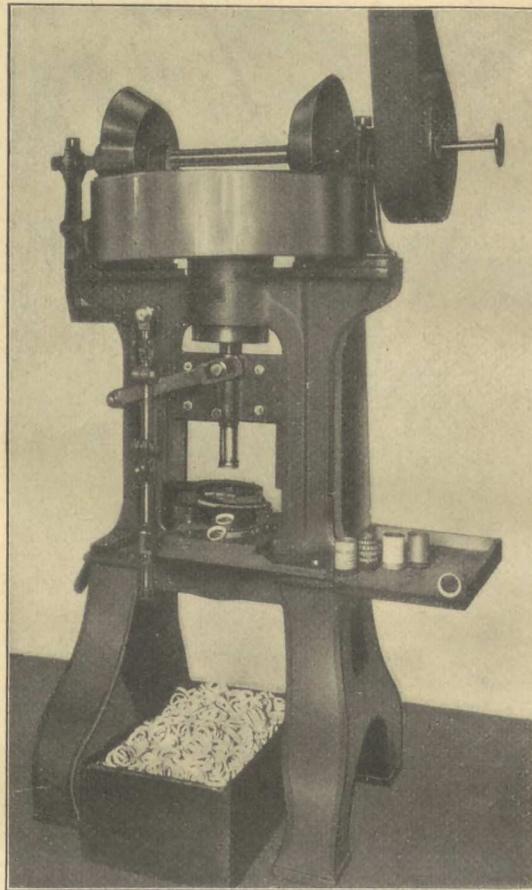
Mit Gas geheizte Rundschachtel-Presse.
